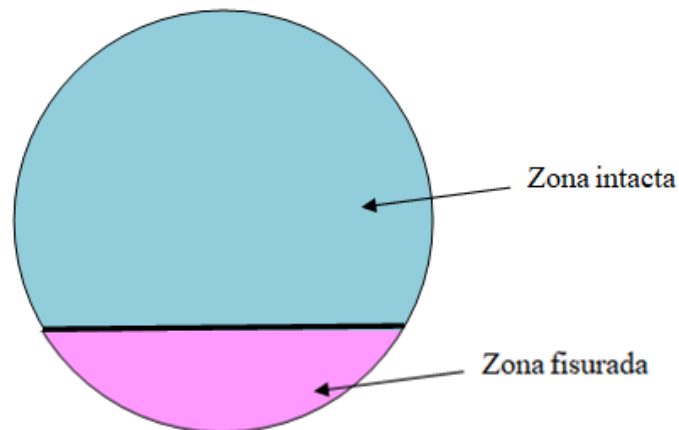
Detalle de la zona fisurada y la zona intacta.
